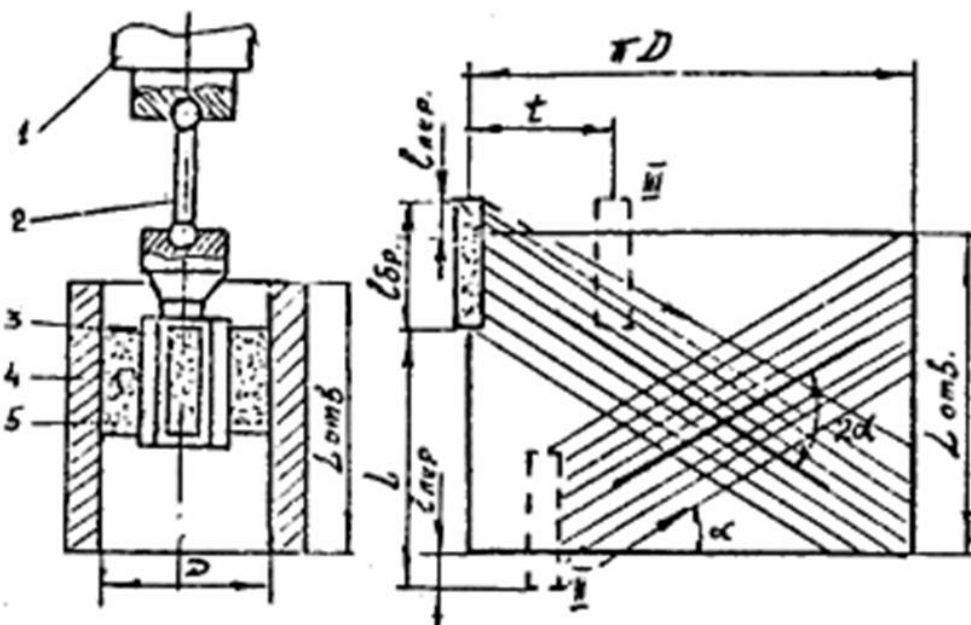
Схема процесса хонингования: 1 – шпиндель станка; 2 – шарнирное устройство; 3 – хонинговальная головка; 4 – гильза; 5 – хонинговальные бруски; α – угол подъема следов абразивных зерен; II, III – крайние положения бруска за один двойной ход
